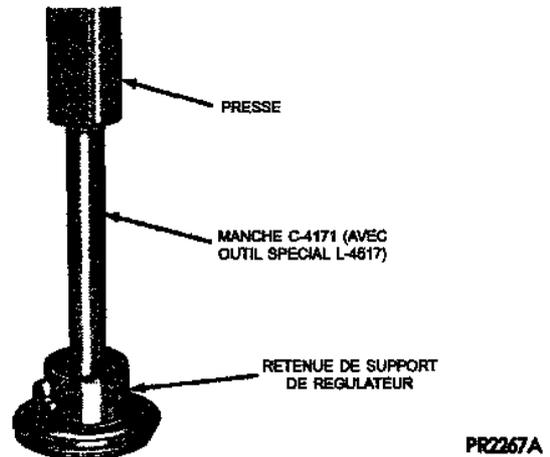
Dépose de la cuvette de roulement de la retenue du support du régulateur
